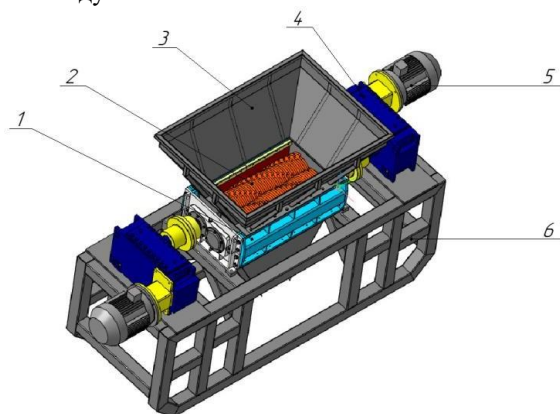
Двухроторный шредер: 1- блок измельчения; 2- ротор с режущими ножами; 3- загрузочное окно; 4- редуктор; 5- электродвигатель; 6- рама.
